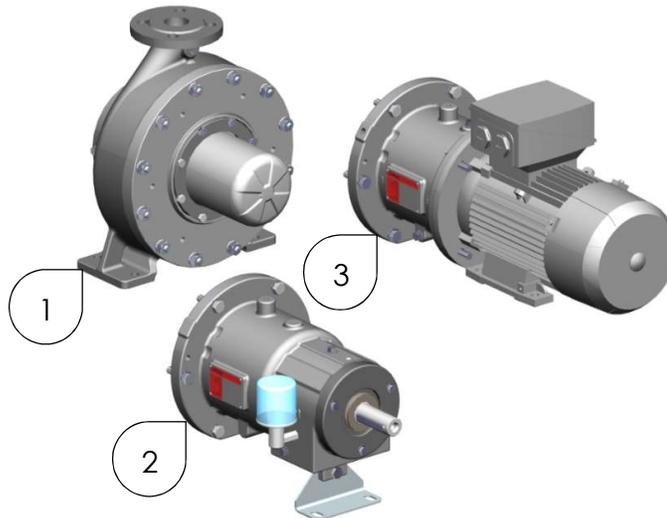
Vista en 3D de la voluta contenida (1), el extremo del motor CBMM (2) y el extremo del motor CBME (3)
